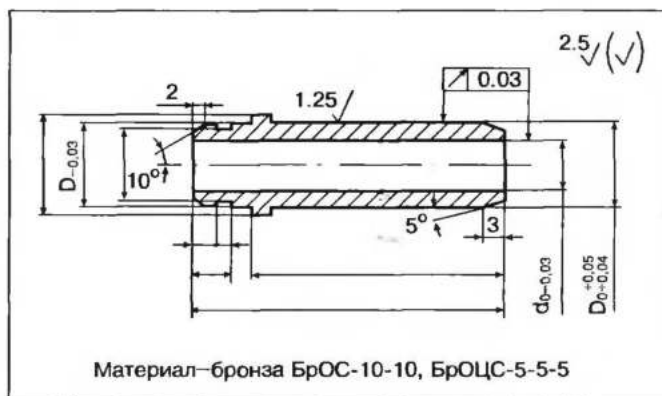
Типовой эскиз направляющей втулки: D_0 — диаметр гнезда в головке блока; d_0 — диаметр стержня клапана; D — посадочный диаметр маслоотражательного колпачка
